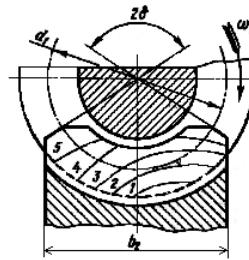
Схема расположения контактных линий (1...5) в процессе зацепления червячной пары.
